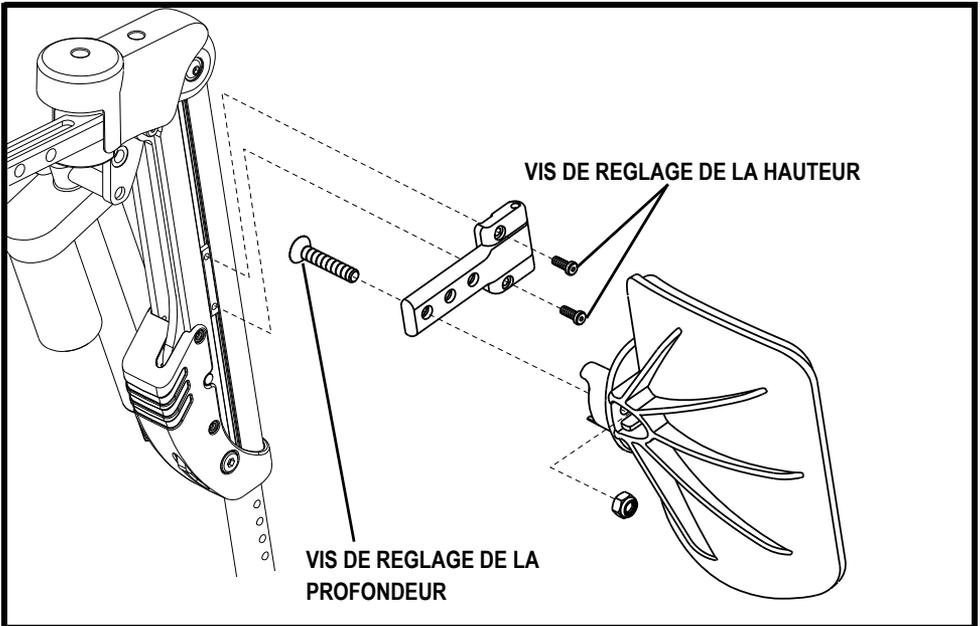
Réglages des coussins de mollet rétractables (ALR montré)
